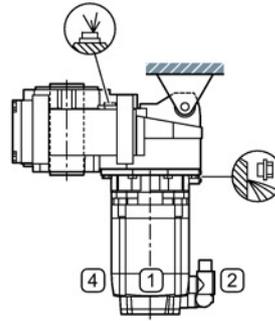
Einbautagen für Flachgetriebe FZ.F und FD.F (Flansch-) und FZ.Z und FD.Z (Gehäuseflanschausführung), Baugrößen 39 - 129, 2-stufig und 3-stufig
